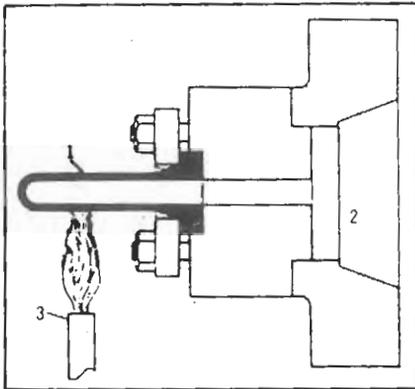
Encendido por tubo incandescente. 1. Tubo. 2. Cámara de explosión. 3. Mechero.
